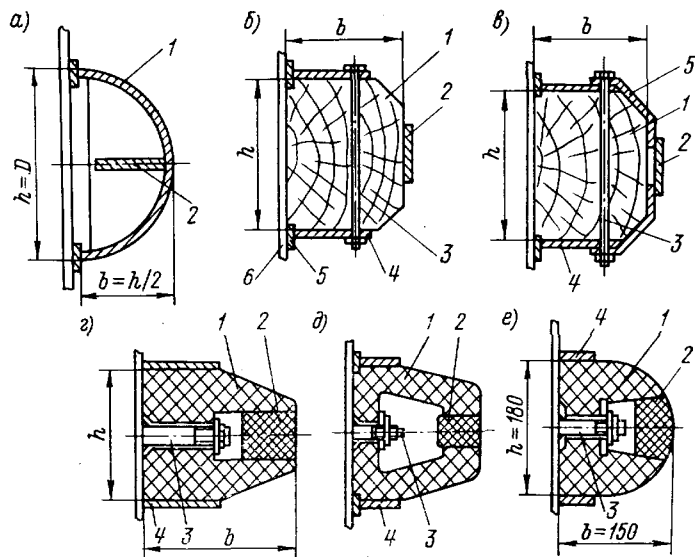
Сечения привальных брусьев: а — металлический жесткий; б, в — деревянный полужесткий; г, д, е — резиновый мягкий. 1 — привальный брус; 2 — полоса; 3 — болт; 4 — коробка привального брусья; 5 — обойма; 6 — обшивка корпуса судна.
